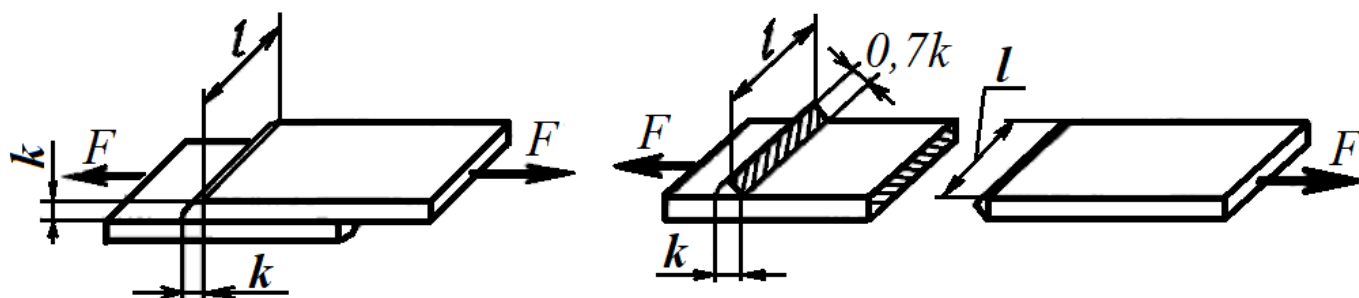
Схема нагружения лобового углового сварного шва силой F
